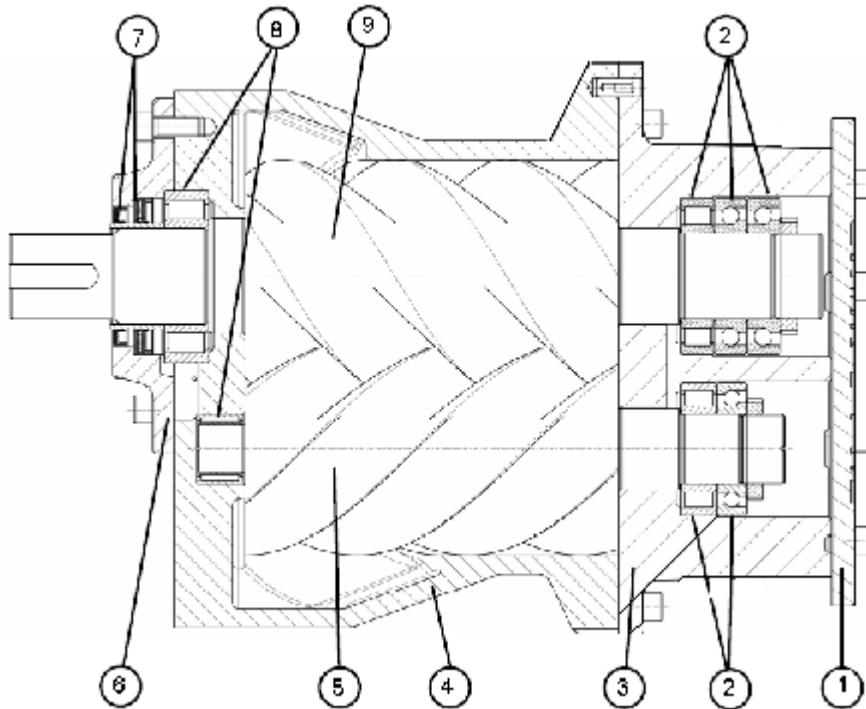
Устройство винтового компрессорного модуля OS70
